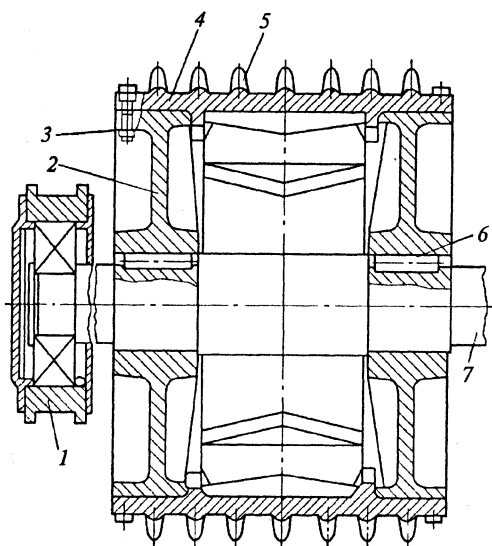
Валок двухвалковой зубчатой дробилки
